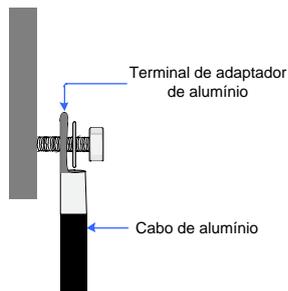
Sequência de conexão do terminal de cabo de alumínio
